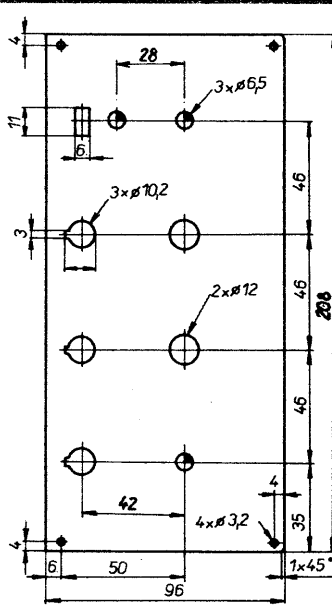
Zadný panel, mat. dural hr. 3 mm
